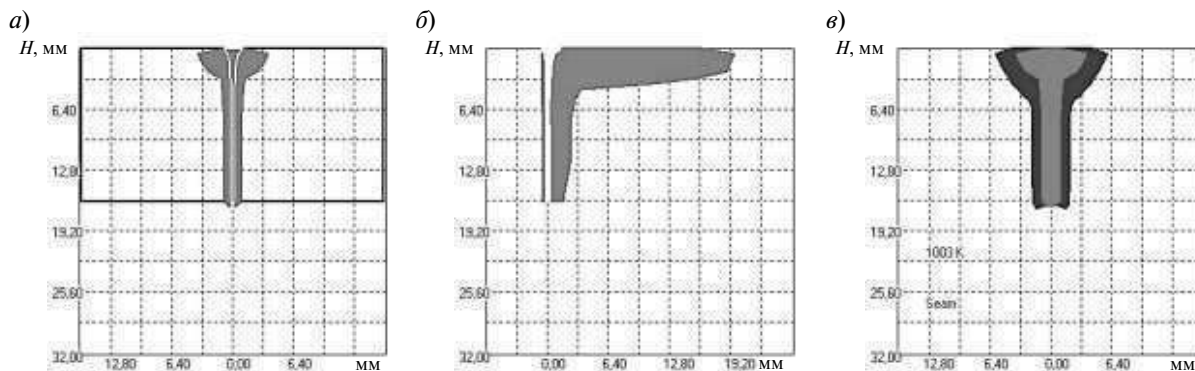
Лазерно-дуговая сварка в нижнем пространственном положении: *a* — зона проплавления; *б* — сварочная ванна (продольный вид), *в* — сварное соединение
